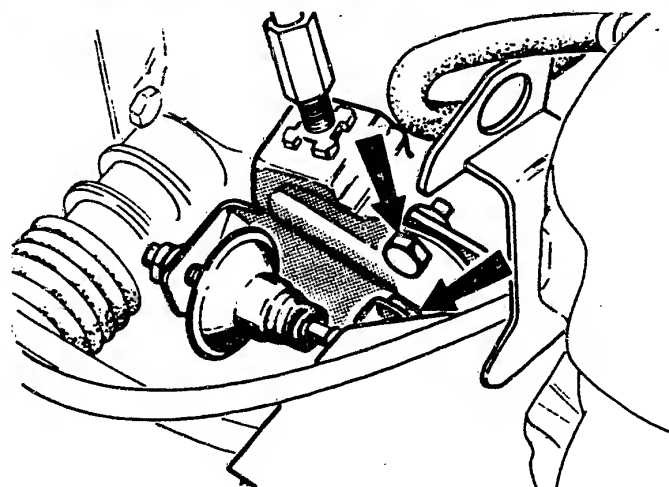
Automatikgetriebe (ATX): Der Halter ist abzuschrauben, um das Rückschaltgestänge besser von der Welle abziehen zu können.
